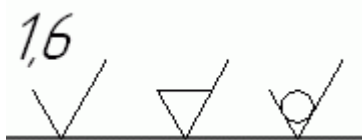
Примеры обозначения шероховатости в КОМПАС
